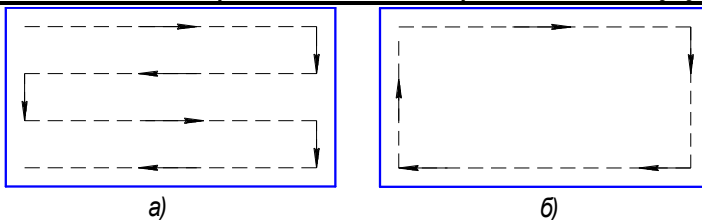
Траєкторії відносного руху інструмента і заготовки:
